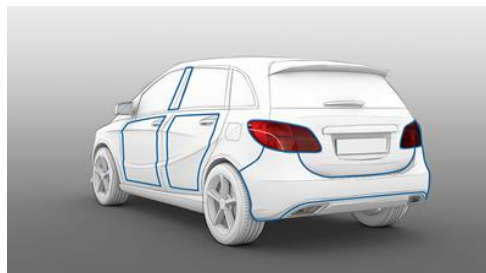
Auch große Kunststoff-Bauteile beispielsweise im oder am Auto lassen sich mit Lasertechnologie schweißen.
